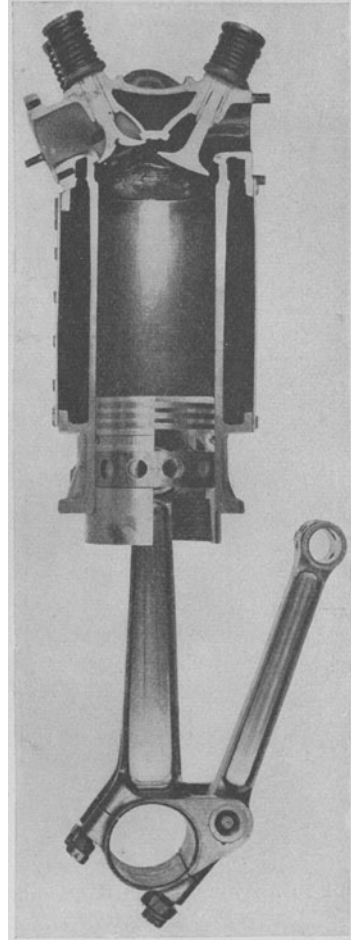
Zylinder des Sunbeam-Flugmotors.
